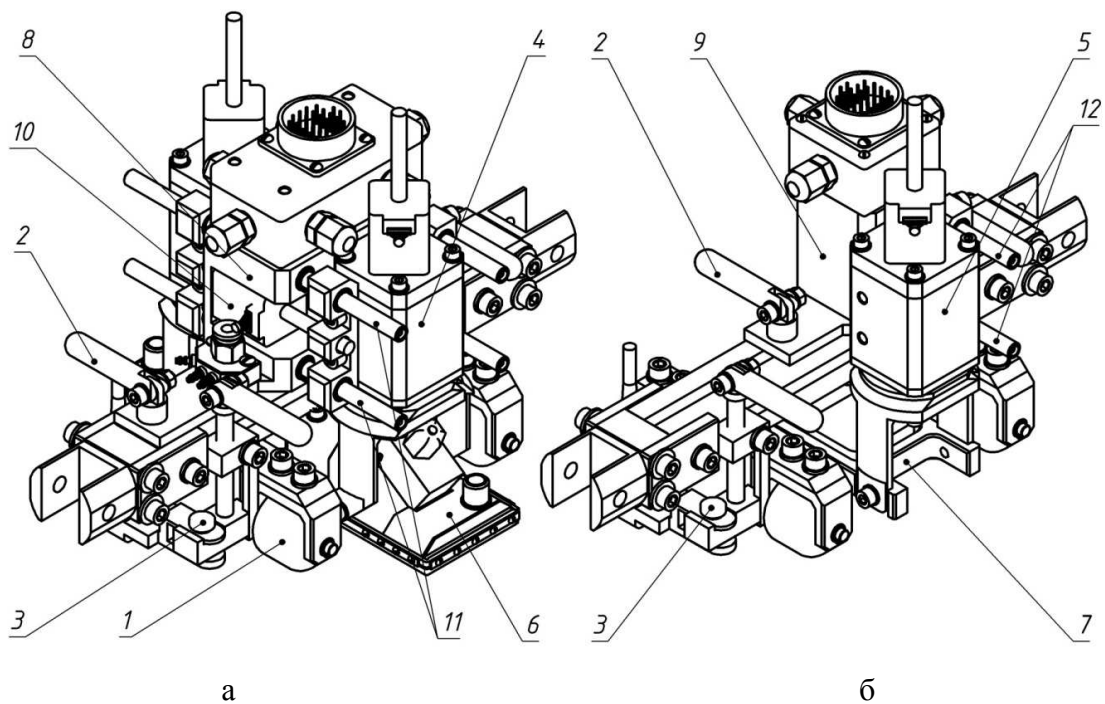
Общий вид сканера: а) акустического контроля; б) вихретокового контроля.
